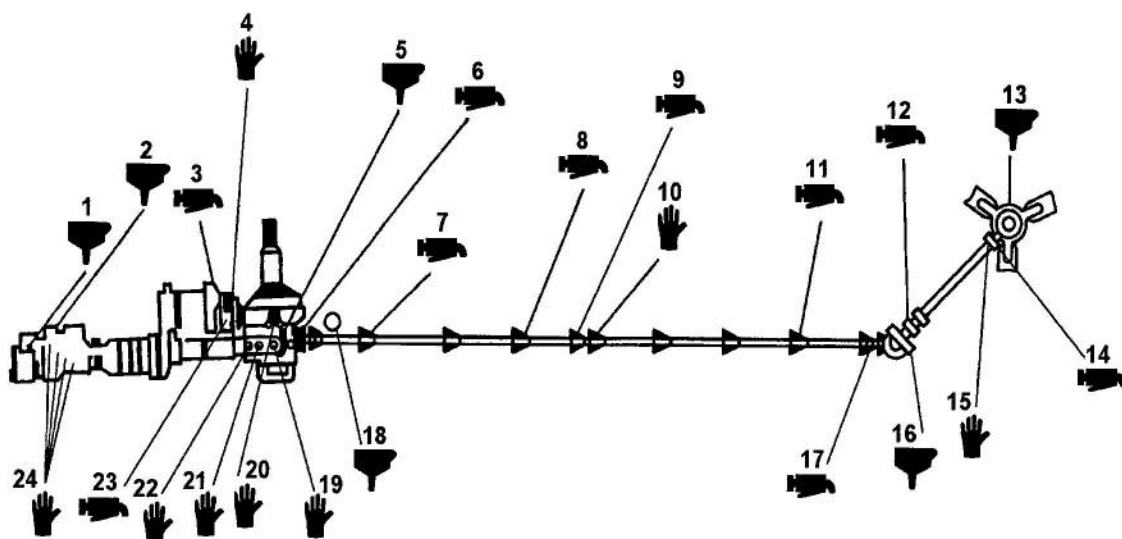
Смазка агрегатов двигателей и трансмиссии
